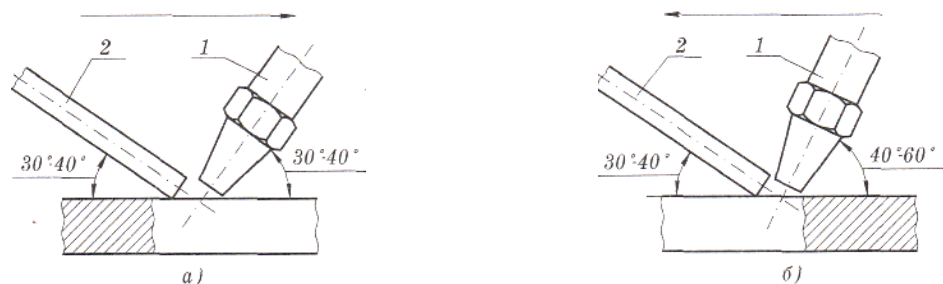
Схема направления перемещения горелки и присадочного прутка а) правое направление горелки и прутка, б) левое направление горелки и прутка, 1– присадочный материал, 2 – мундштук горелки.
